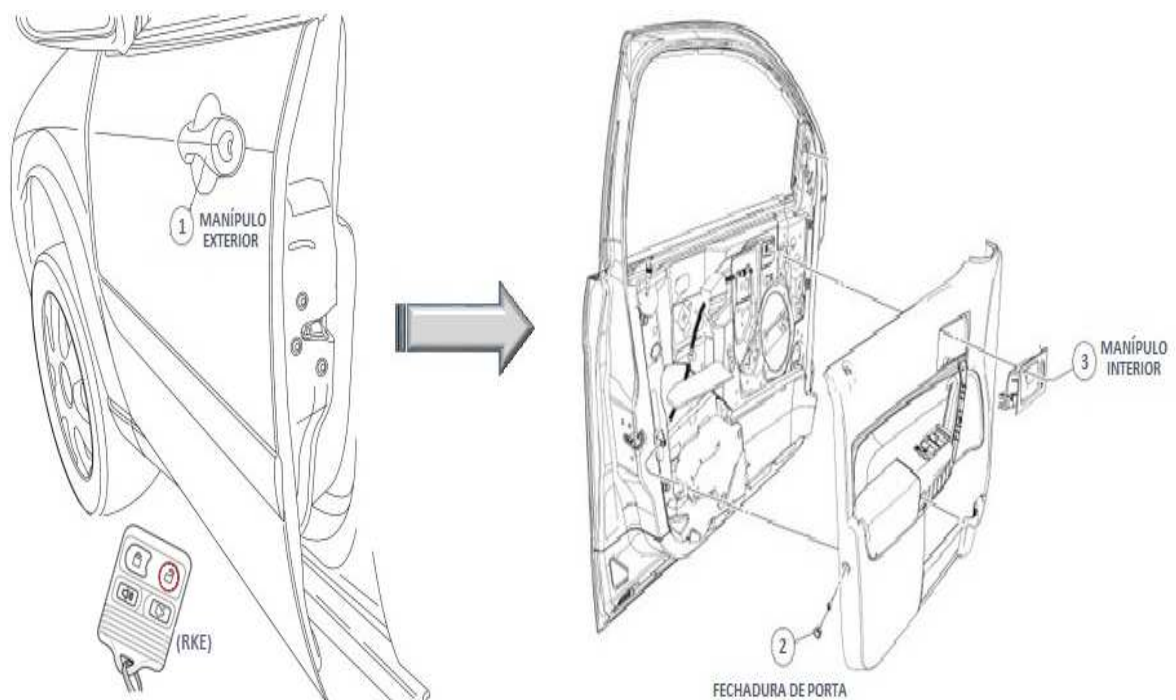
Vista Explodida do Exterior/Interior da porta (Adaptado de ffguide.net)
